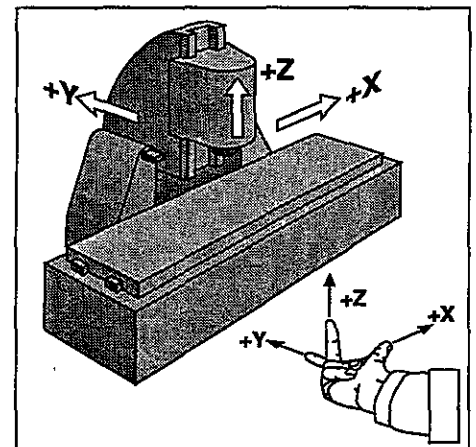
Désignation et sens des axes de la machine sur une fraiseuse
